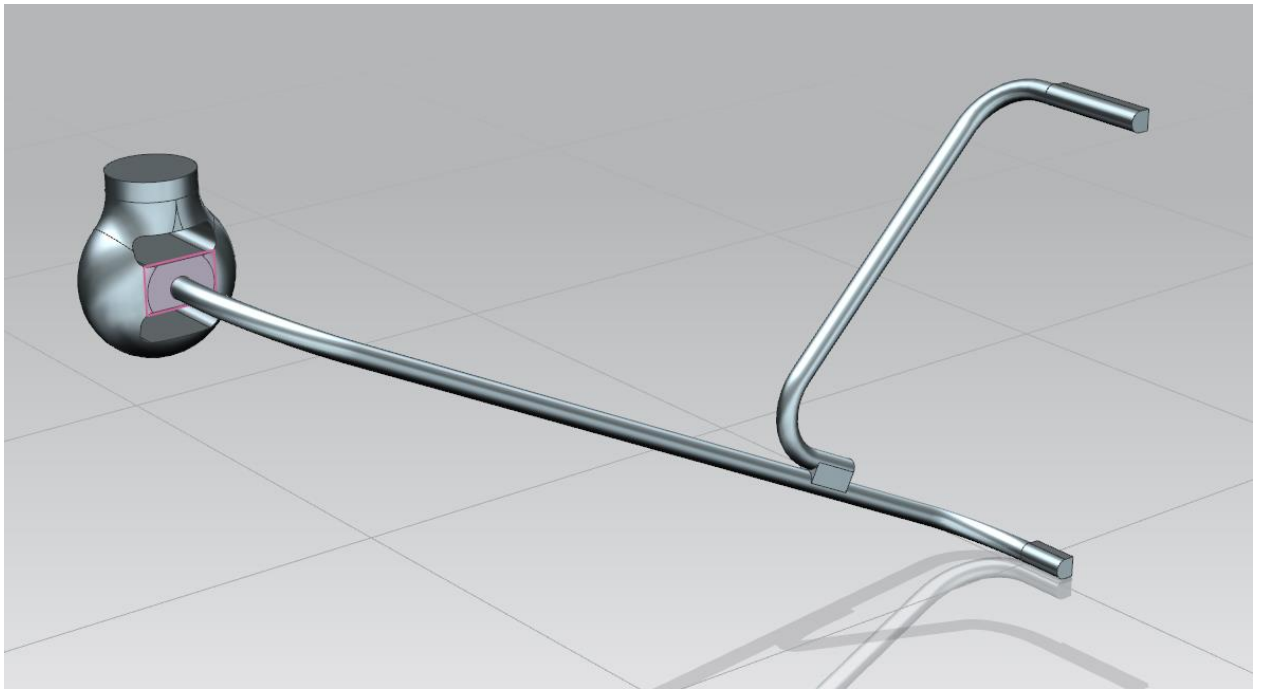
Модель кронштейна с местами сварки и резиновым буфером
